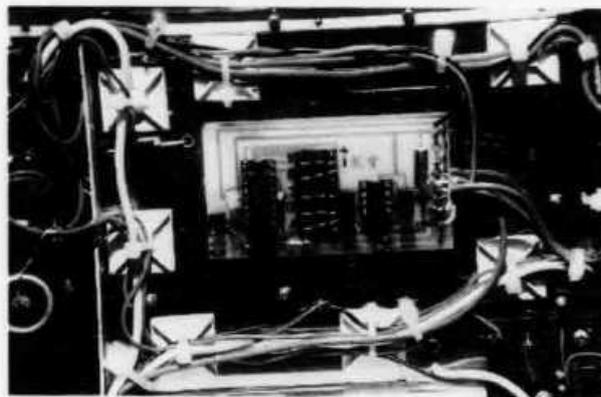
La place nécessaire à son montage a été trouvée sous le châssis du Transceiver QRP construit pour la bande CW du 10 Mc.
